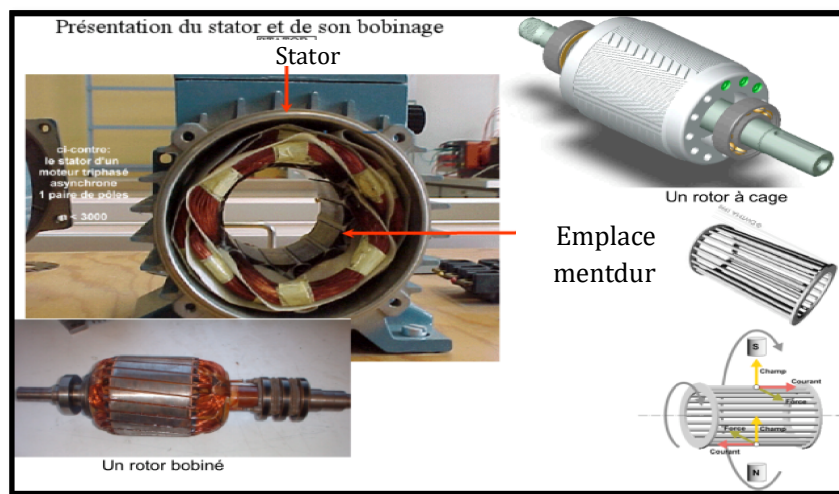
Machine asynchrone à rotor bobiné et à rotor à cage.
